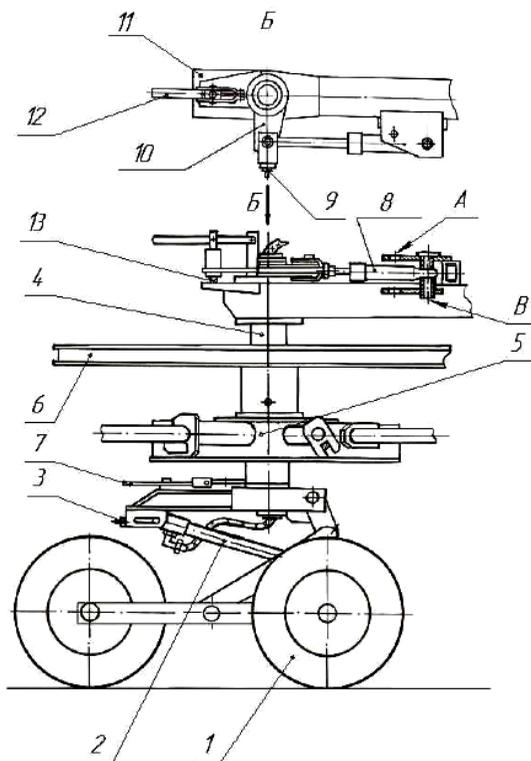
Установка заднего ротора: 1 – ходовая система; 2, 8 – гидроцилиндры; 3 – регулируемый упор; 4 – ось; 5 – корпус ротора; 6 – шкив; 7 – рычаг с фиксатором; 9 – гайка регулировочная; 10 – рычаг поворота ходовой системы; 11 – сектор; 12 – рукоятка; 13 – фиксатор
